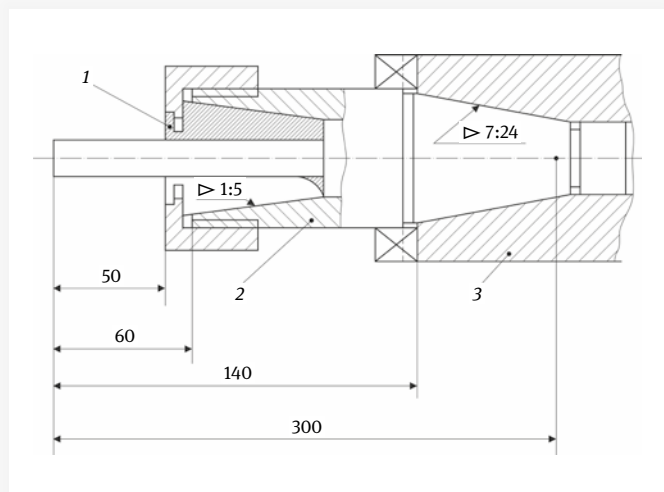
Цанговый патрон с закрепленной оправкой: 1 – цанга; 2 – корпус патрона; 3 – шпиндель станка
